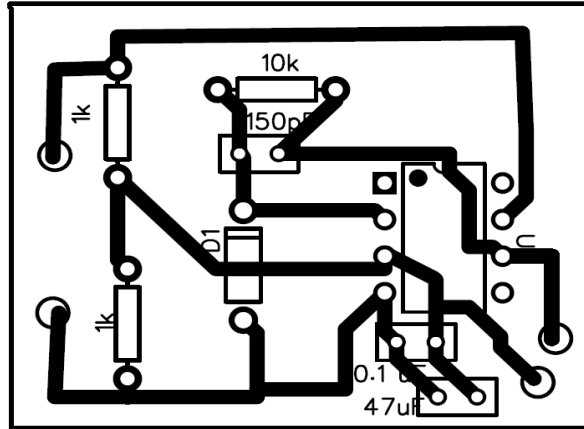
Placa PCB donde se montó el circuito del fotodetector. Las dimensiones de la placa son 30x40 mm.
